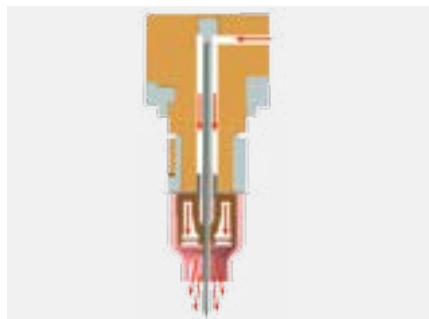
Линза в сварочной горелке обеспечивает ламинарный поток защитного газа
